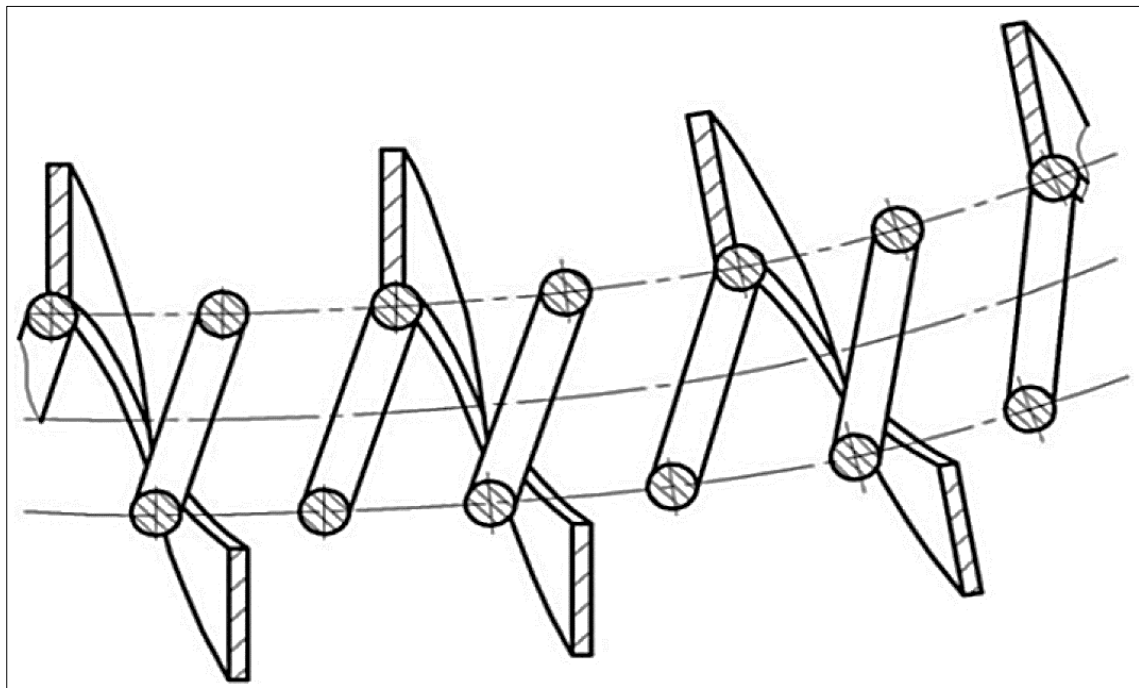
Робочий орган з прутковою несучою та смуговою робочою спіралями
